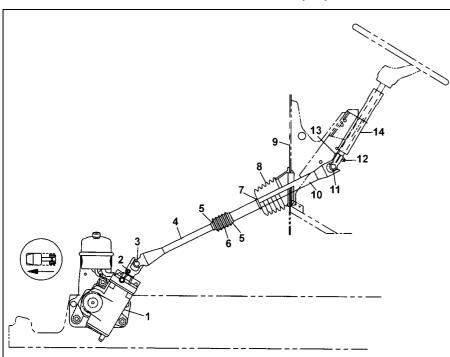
Карданная передача рулевого управления. 1 - рулевой механизм, 2 - стяжной болт, 3 - нижний карданный шарнир, 4 - внутренний вал, 5 - хомут чехла, 6 - нижний чехол карданной передачи, 7 - втулка верхнего чехла карданной передачи, 8 - верхний чехол карданной передачи, 9 - перегородка моторного отсека, 10 - внешний вал, 11 - верхний карданный шарнир, 12 - гайка стяжного болта, 13 - стяжной болт, 14 - рулевая колонка.
